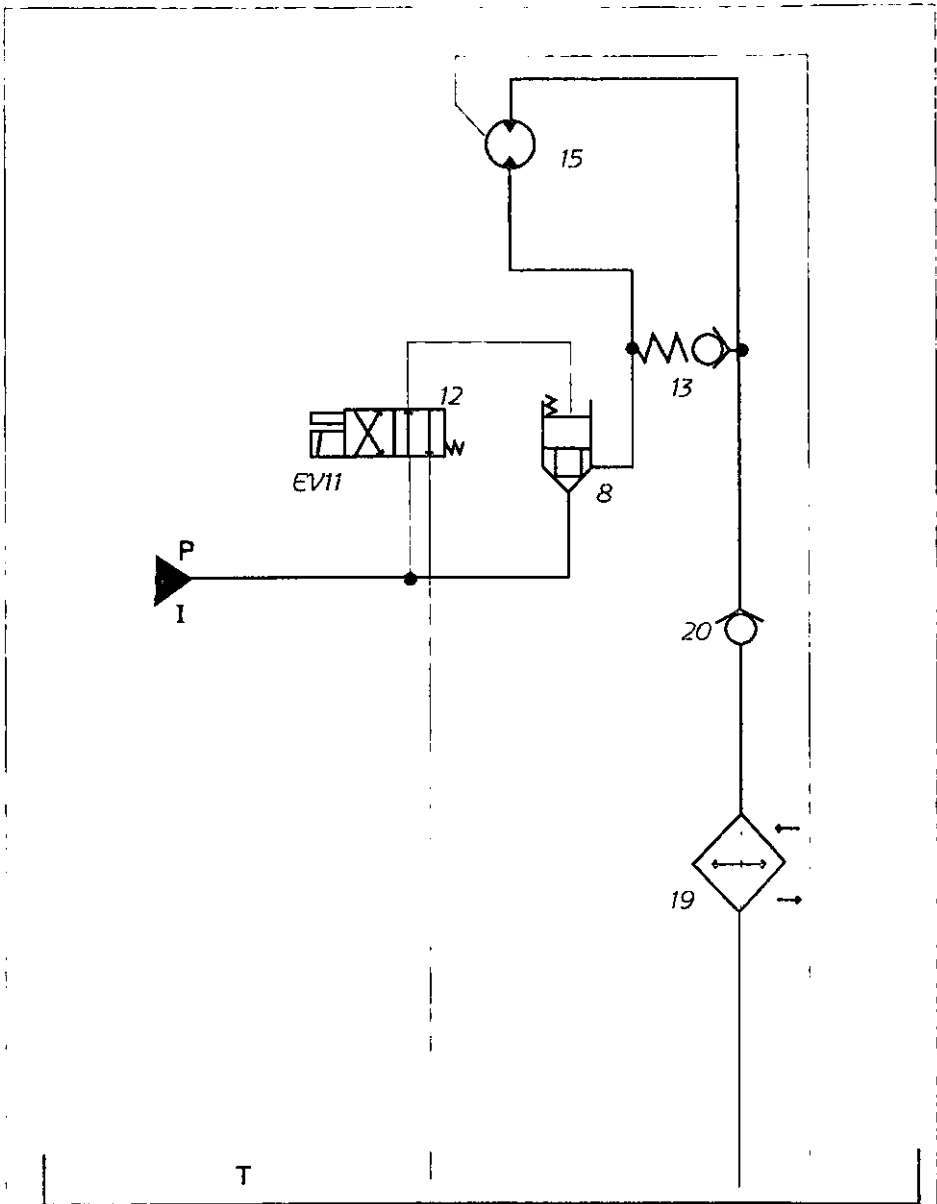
Conjunto del motor hidráulico del tornillo.
